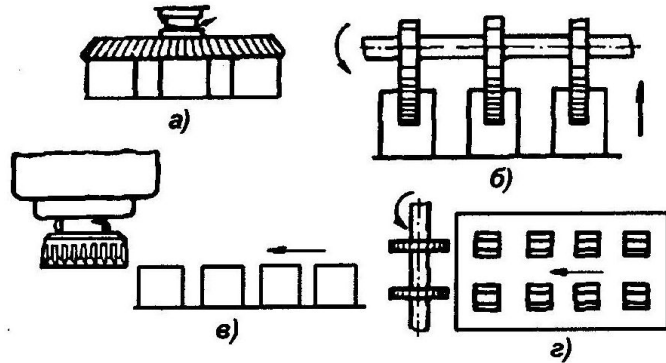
Схеми фрезерування заготовок встановлених рядами
